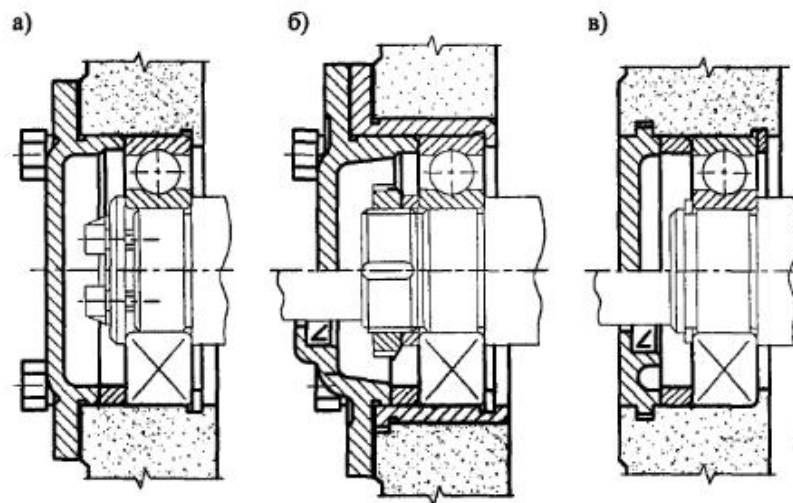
Установка наружного кольца неразъемного подшипника в корпусе фиксирующей опоры
